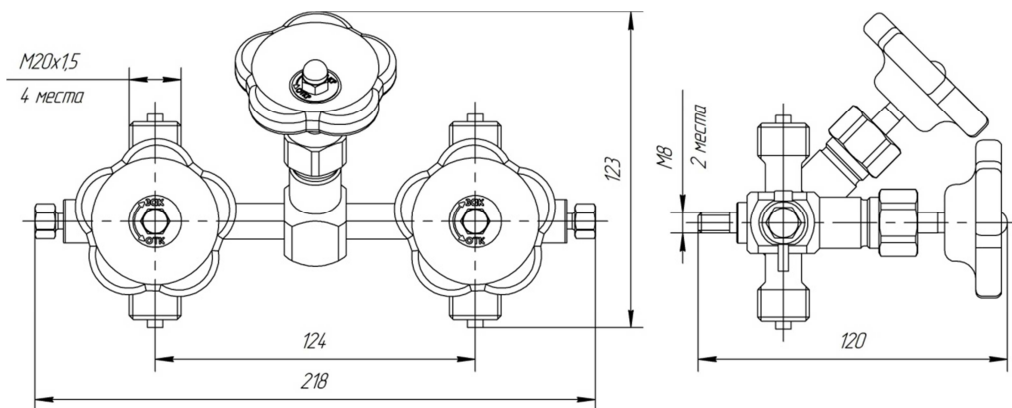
Габаритно-присоединительные размеры изделия 4xВИГ160ДФ-Н1Б1Б-1
